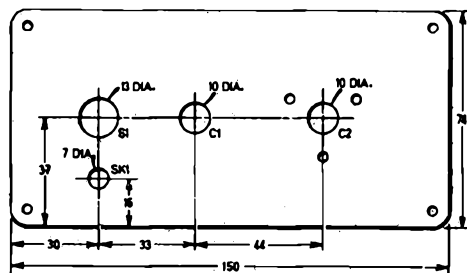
Piano di foratura del pannello frontale della scatoletta di plastica all'interno della quale viene installato il ricevitore. Le misure sono in millimetri.
